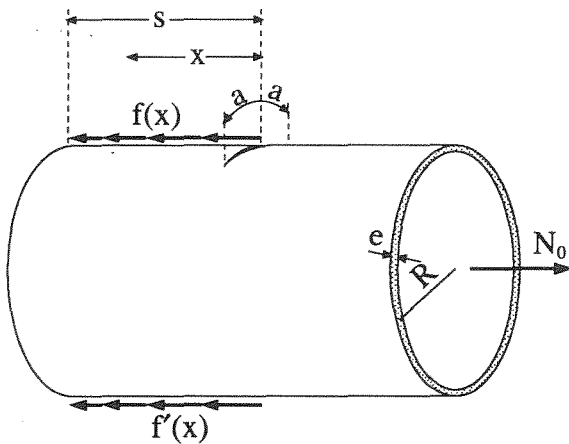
Cargas y fisura en el detalle constructivo.
